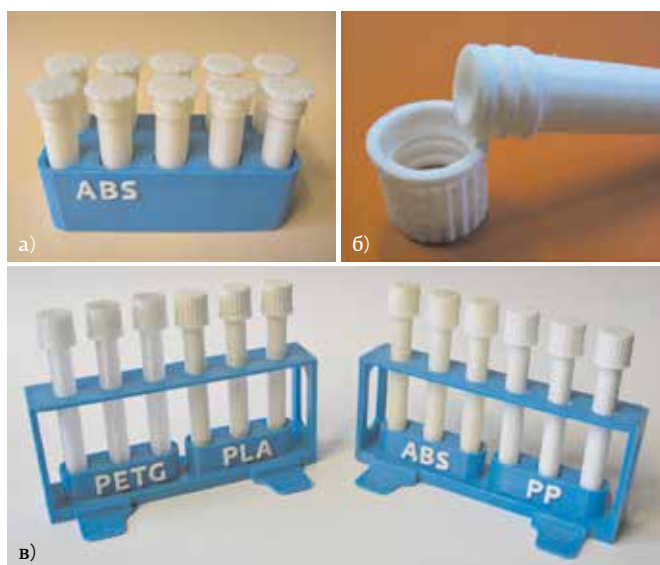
Пробирки, напечатанные из различных типов пластика: а – короткие пробирки с безрезьбовыми крышками (ABS); б – резьба с 3D-печатью на внешней стороне трубки и внутри колпачка; в – удлиненные трубки с завинчивающимися крышками, изготовленные из различных материалов [29]
